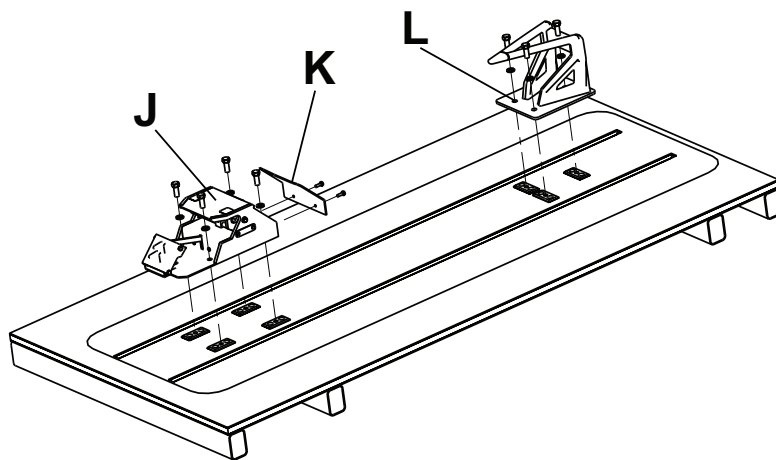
Fixations côté tête et côté pieds - installation sur plaque de plancher
